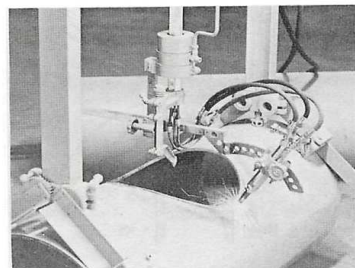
Machine portable pour l'usinage des piquages su tubes ou sur réservoirs.
